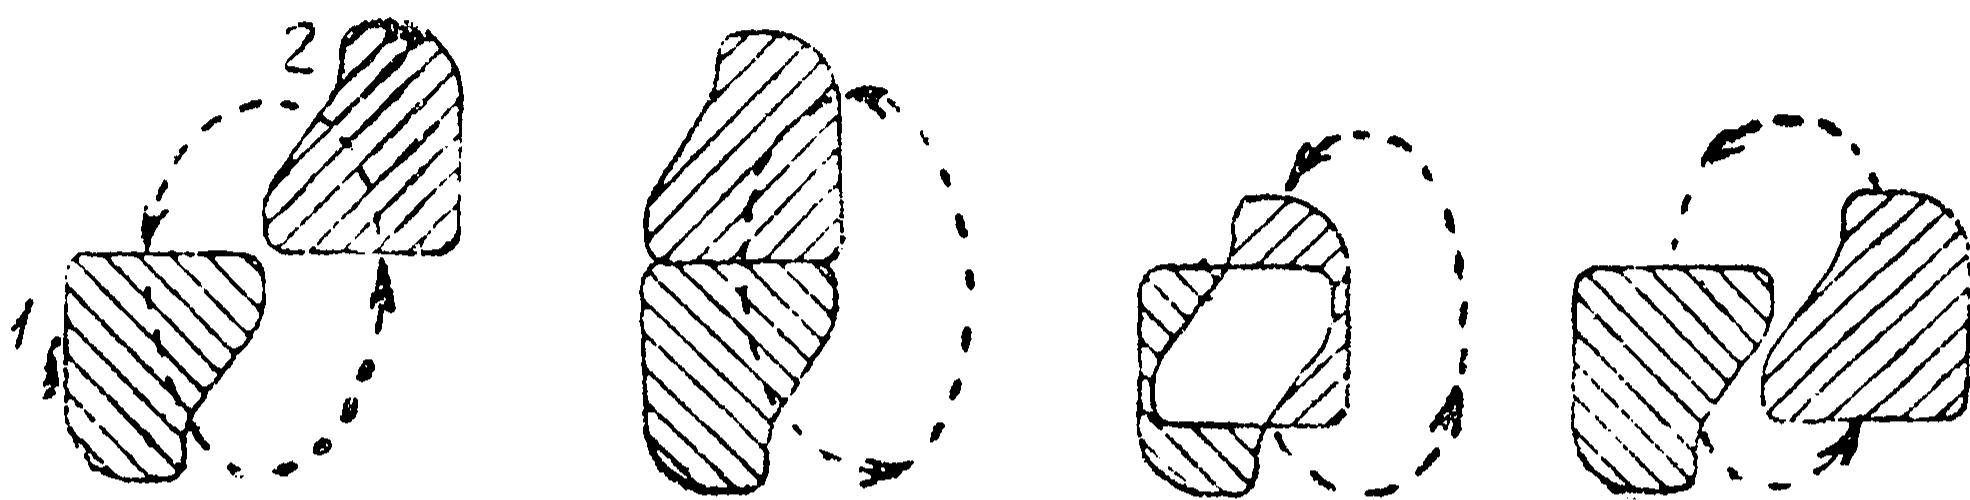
Детали золотникового газораспределения Barr & Straud.
